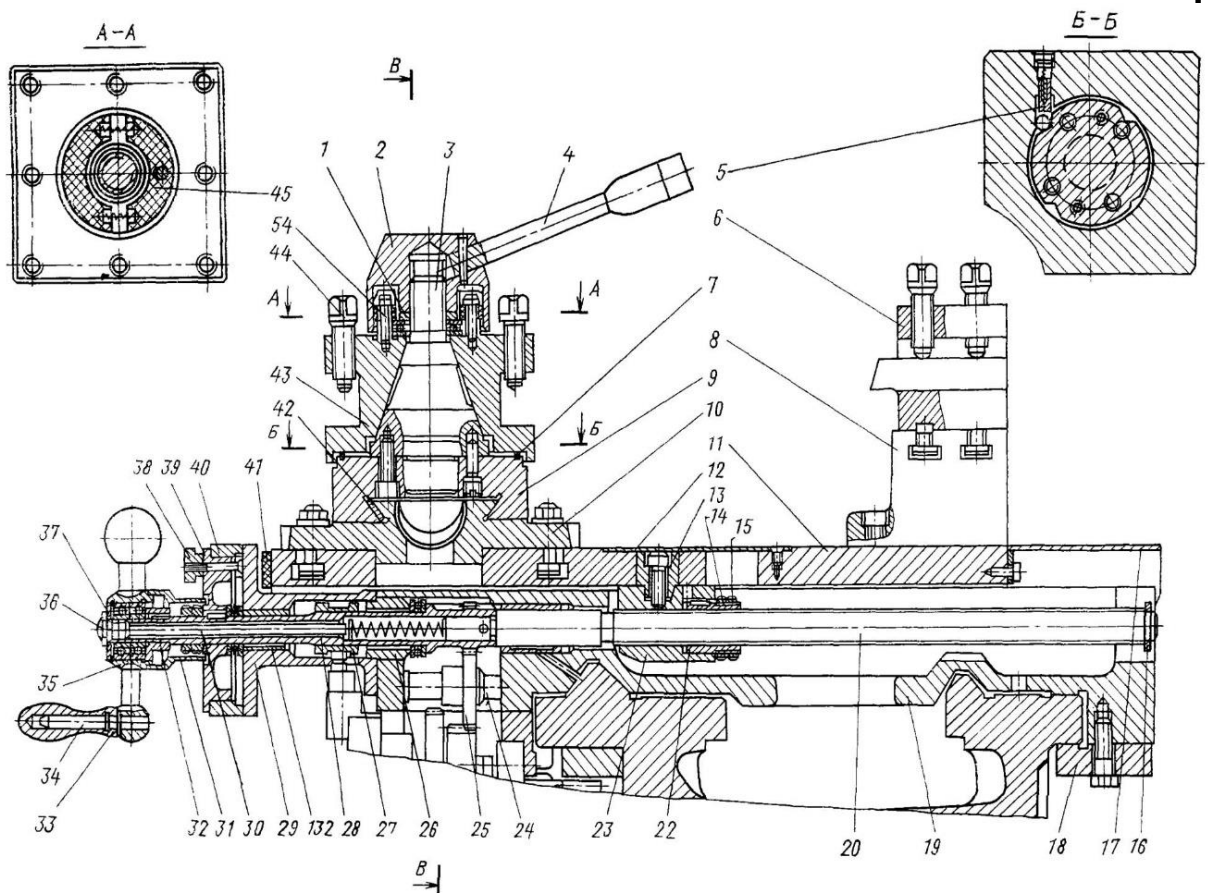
Супорт токарно-гвинторізного верстата 16K20
